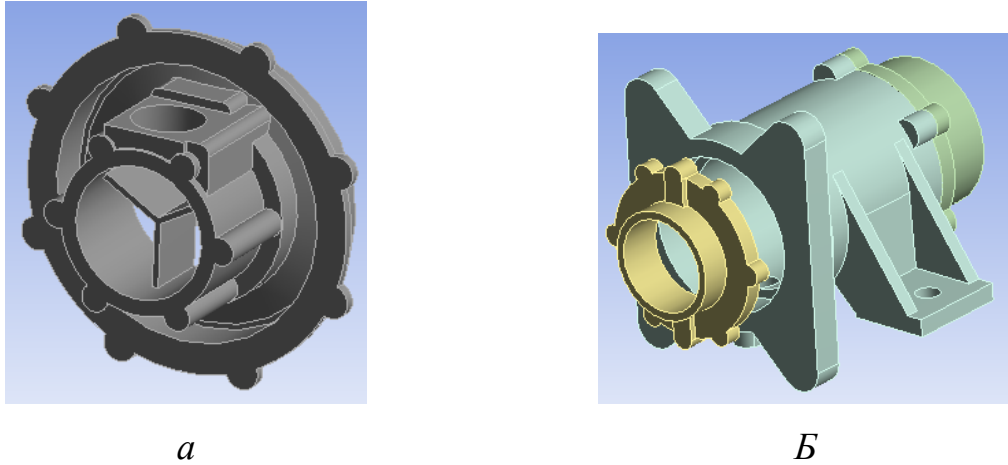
Просторова геометрія корпусних деталей насоса ПН-40УВ
